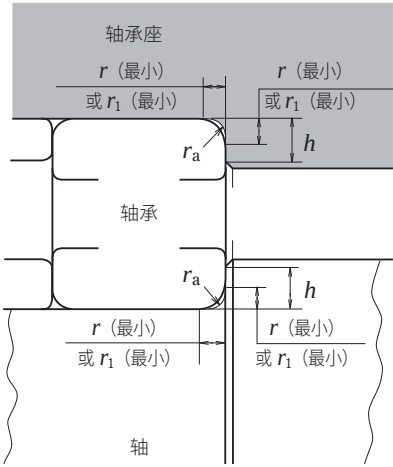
向心轴承的倒角尺寸与轴及轴承座的圆角半径，以及挡肩高度
